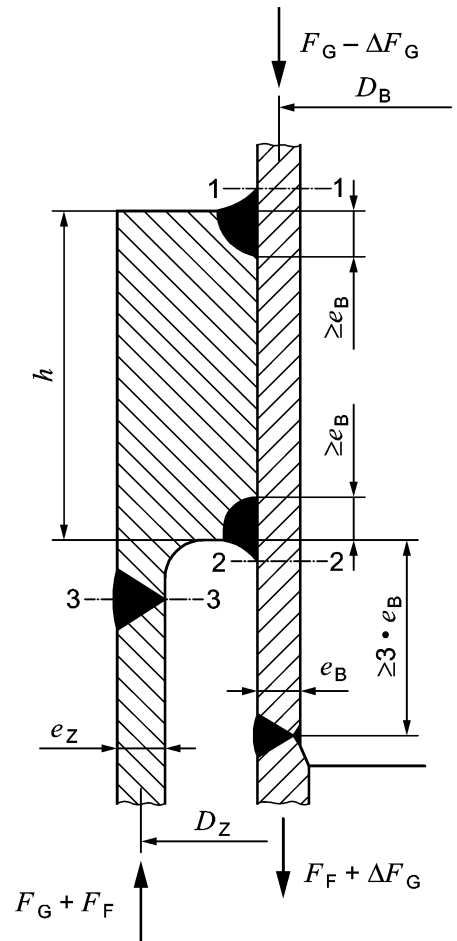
Konstruktionsform A – Zargenanschluss über Tragring im Zylinderbereich
